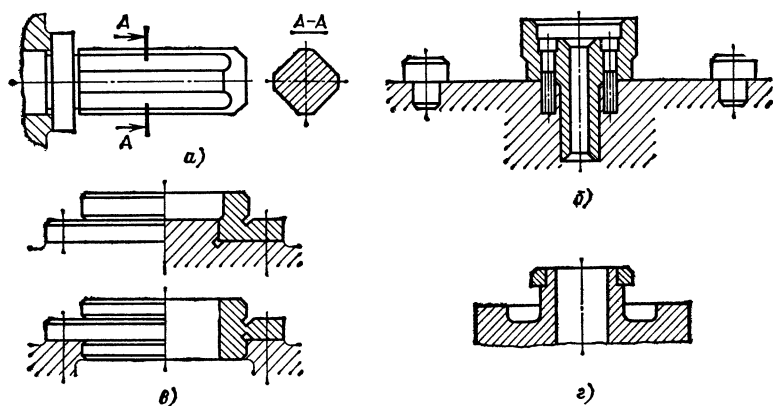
Пальцы для установки заготовки цилиндрическим отверстием:
